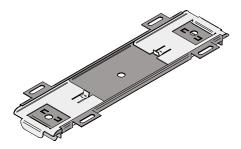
Élément d'assemblage ADRIATIC d-T-MD-4S, pour installation contre le plafond.
